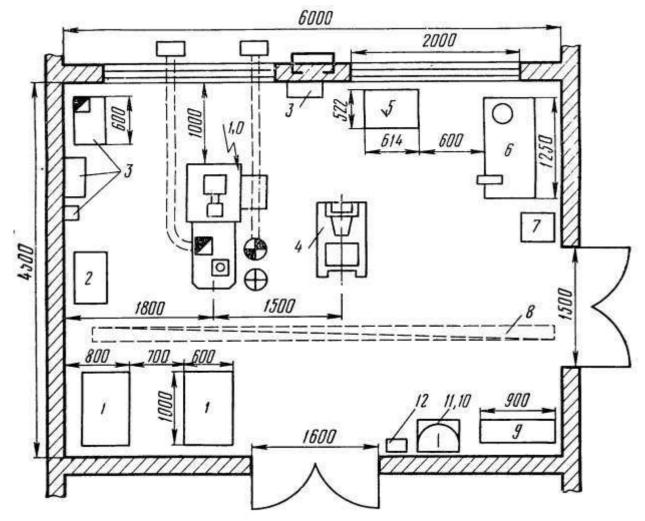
Планировка рабочего места слесаря-обкатчика:
